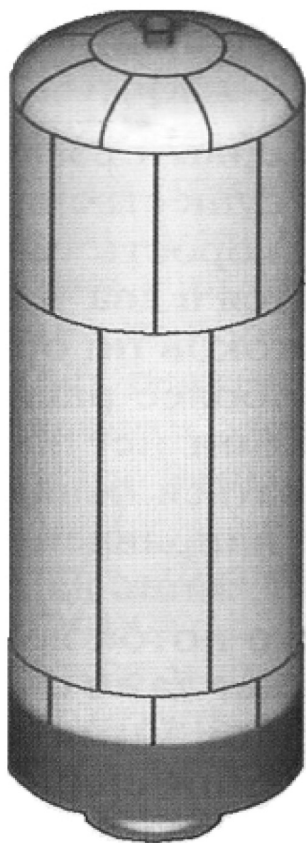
Продольный раскрой стального листа для сварки реактора
